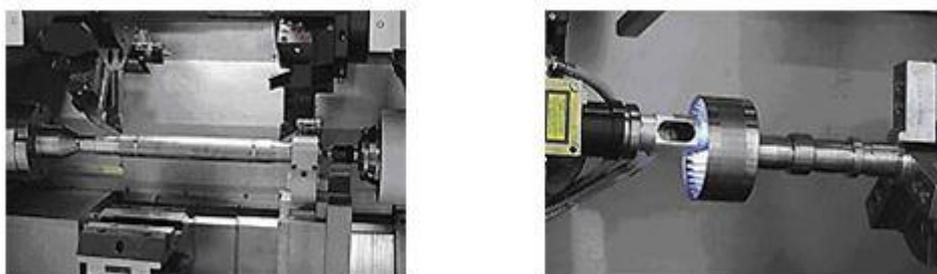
Станки NG 200 DUO фирмы BOEHRINGER. С двумя шпинделями и двумя револьверными головками для одновременной обработки двух деталей
